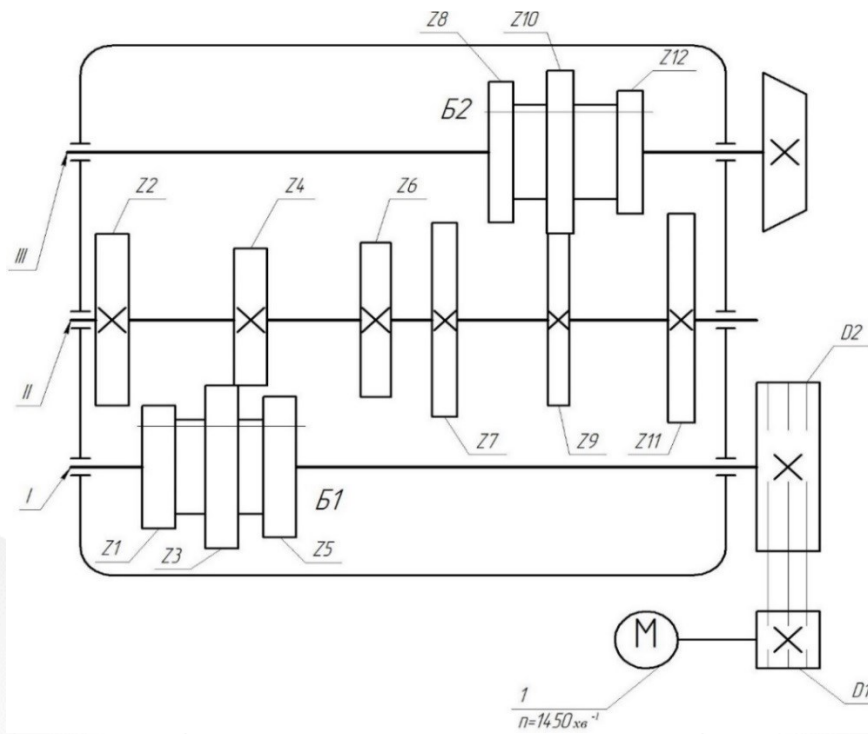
Первісний варіант кінематичної схеми коробки швидкостей верстата
